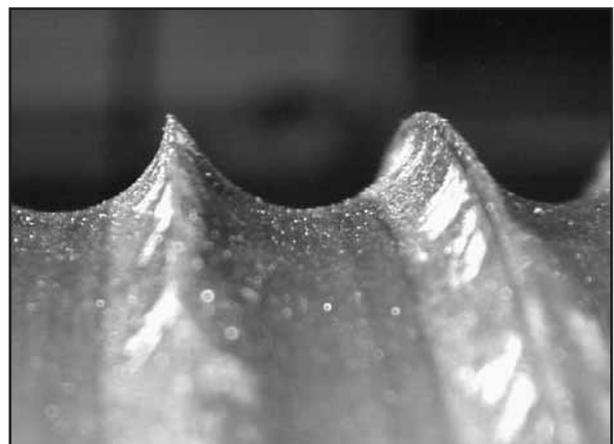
Wenn der einlaufende Seilstrang gegen die Rillenflanke gedrückt wird, verschleiben sowohl die Rille als auch die Seildrähte.
